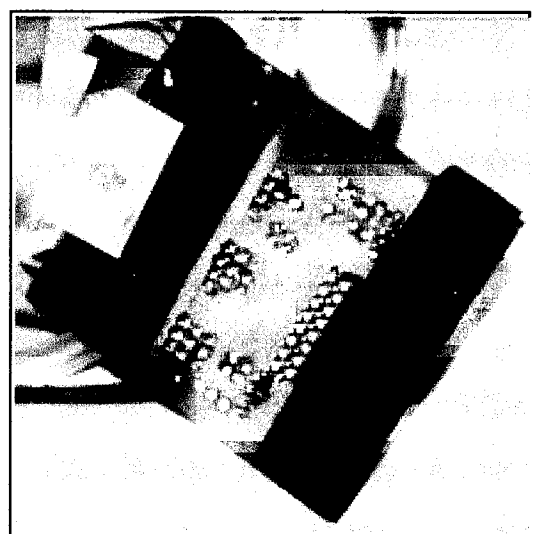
Placa de pré- amplificação, vista pelo lado de soldadura.
